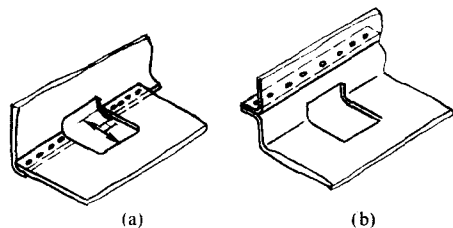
汽车变速箱检查孔处焊缝的布置
